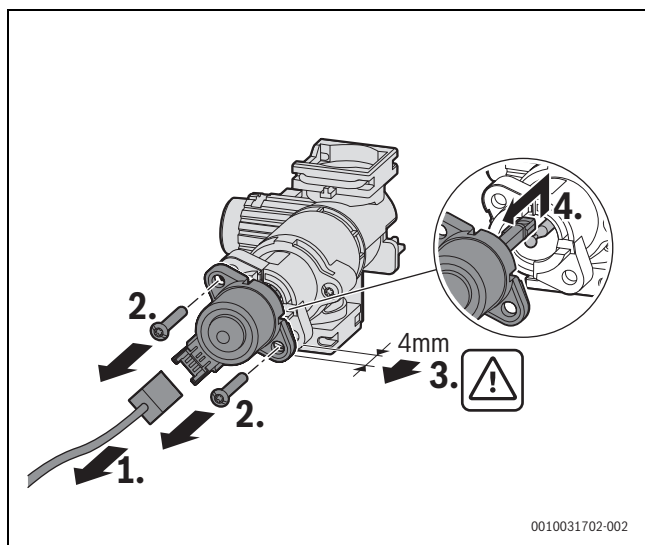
Soltar o motor da válvula de 3 vias (variante com parafusos)
